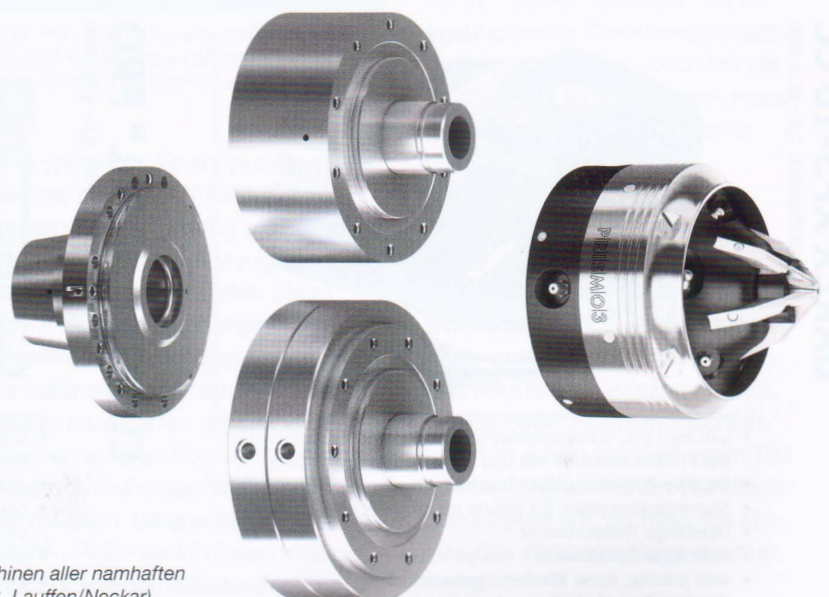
PRISMO3 eignet sich für Werkzeugschleifmaschinen aller namhaften Hersteller (Werkbilder: Schunk GmbH & Co. KG, Lauffen/Neckar)
